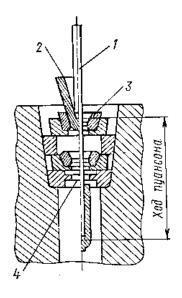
Схема штампа для вытяжки полой поковки через неподвижные кольца: 1 – пуансон; 2 – прошитая заготовка; 3 – первое кольцо; 4 – съемник
